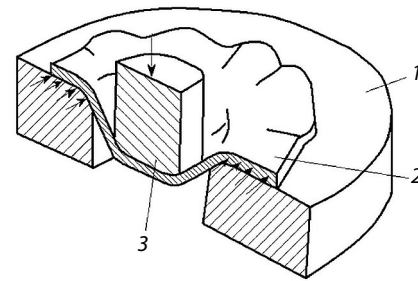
Схема гофрообразования заготовки при статической вытяжке без прижима: 1 — матрица; 2 — заготовка; 3 — пуансон
